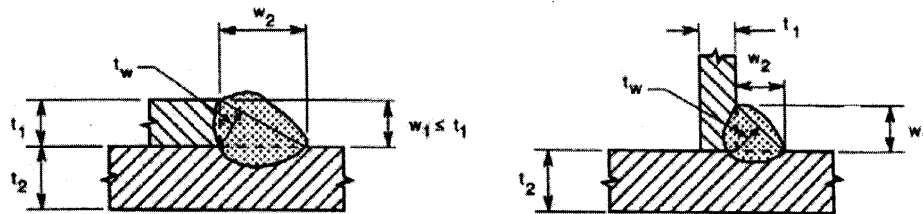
(a) Soldaduras transversales; (b) Soldaduras longitudinales.
